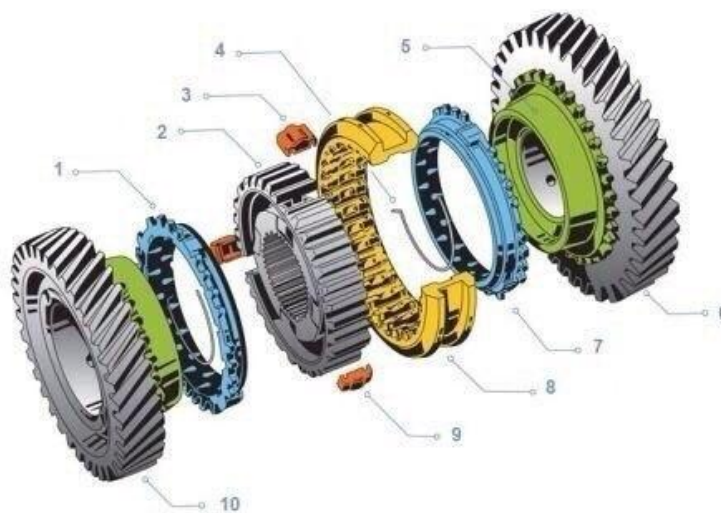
Загальний вигляд та основні елементи синхронізатора коробки передач вантажного автомобіля Renault Premium 430 dxi
